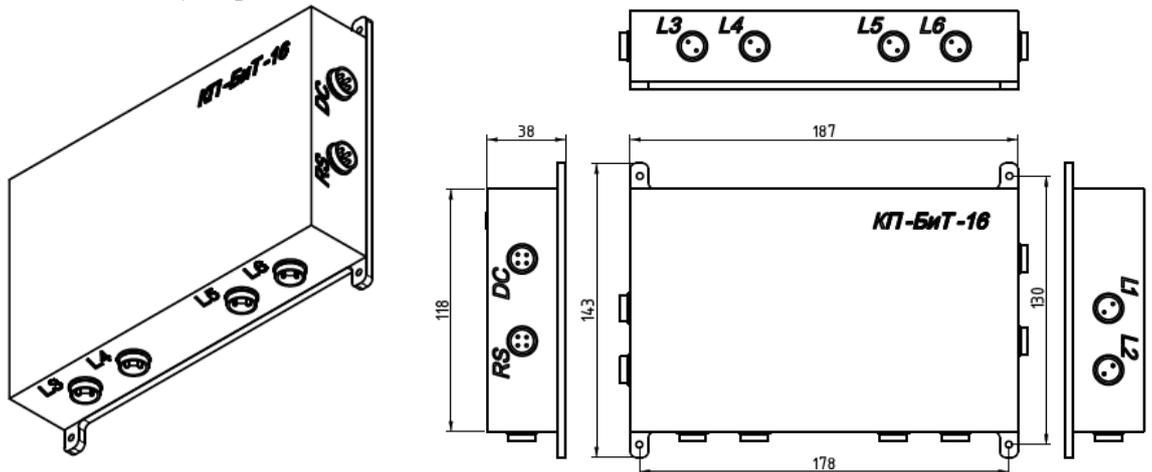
Общий вид, габаритные и присоединительные размеры комму-
